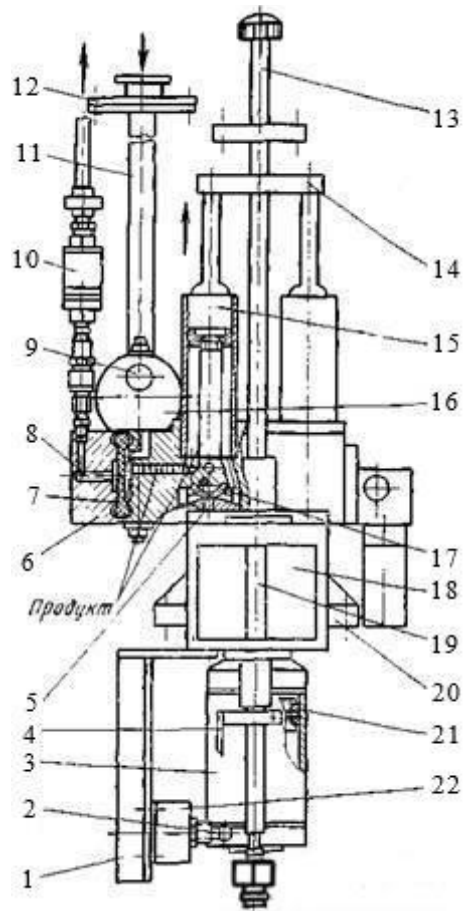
Схема мембранно-поршневого дозатору з вертикальною траєкторією руху поршнів: 1 - пластина; 2 – перемикаючий ролик; 3 - пневматичний циліндр; 4 - рейка; 5 - сопло; 6 - оболонка; 7 - перетинка; 8 - повітряний канал; 9 - індикатор; 10 - дросель; 11 - трубка; 12 - фланець; 13 – регулюючий гвинт; 14 - перемичка; 15 - поршень; 16 - резервуар; 17 - клапан; 18 - оболонка ; 19 - шток; 20 – пластина; 21 - поршень; 22 – перемикач.
